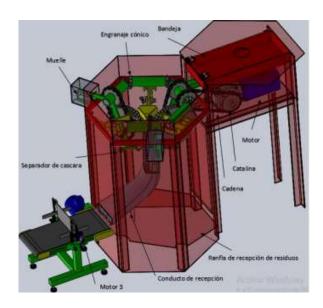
Diseño CAD de la máquina peladora y rebanadora. [3]
